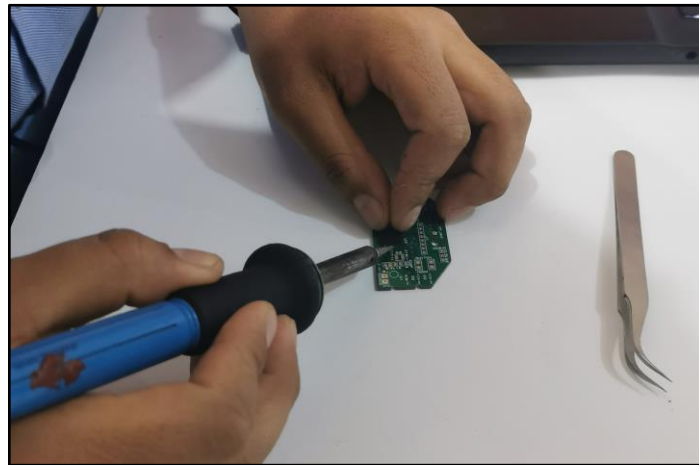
Proceso de soldadura de los componentes electrónicos
